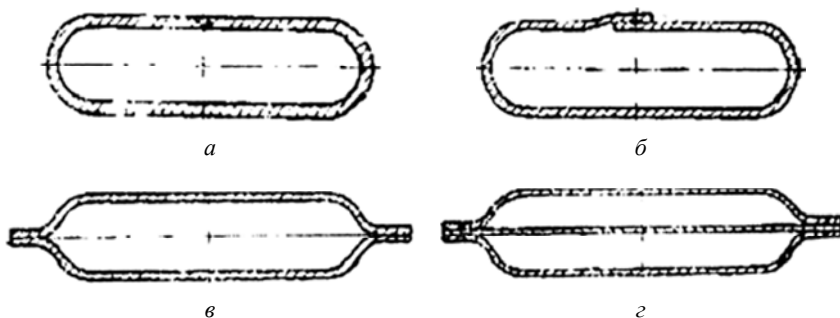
Форма сечения сварных трубчатых пружин
